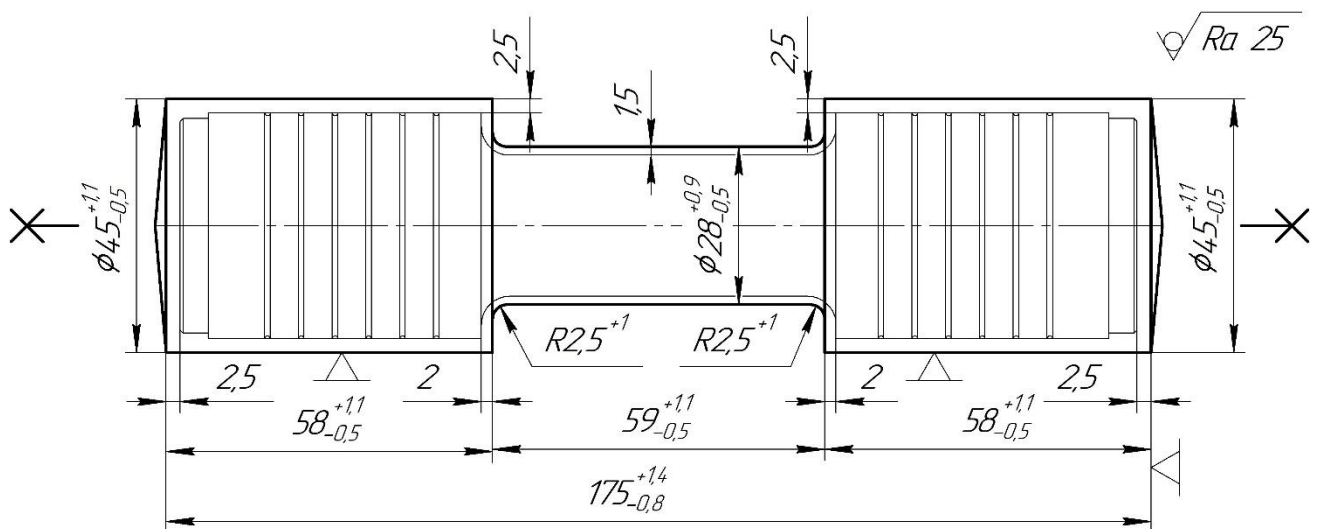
Заготовка, яка виготовлена штампуванням на КГШП
